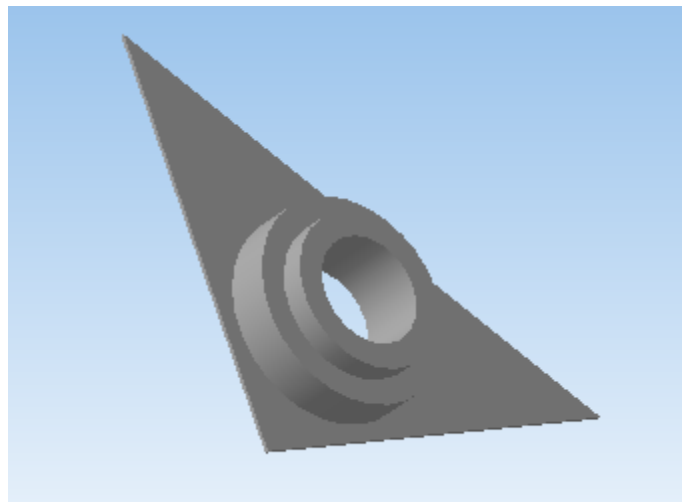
Готова деталь виконана з трикутної заготовки
